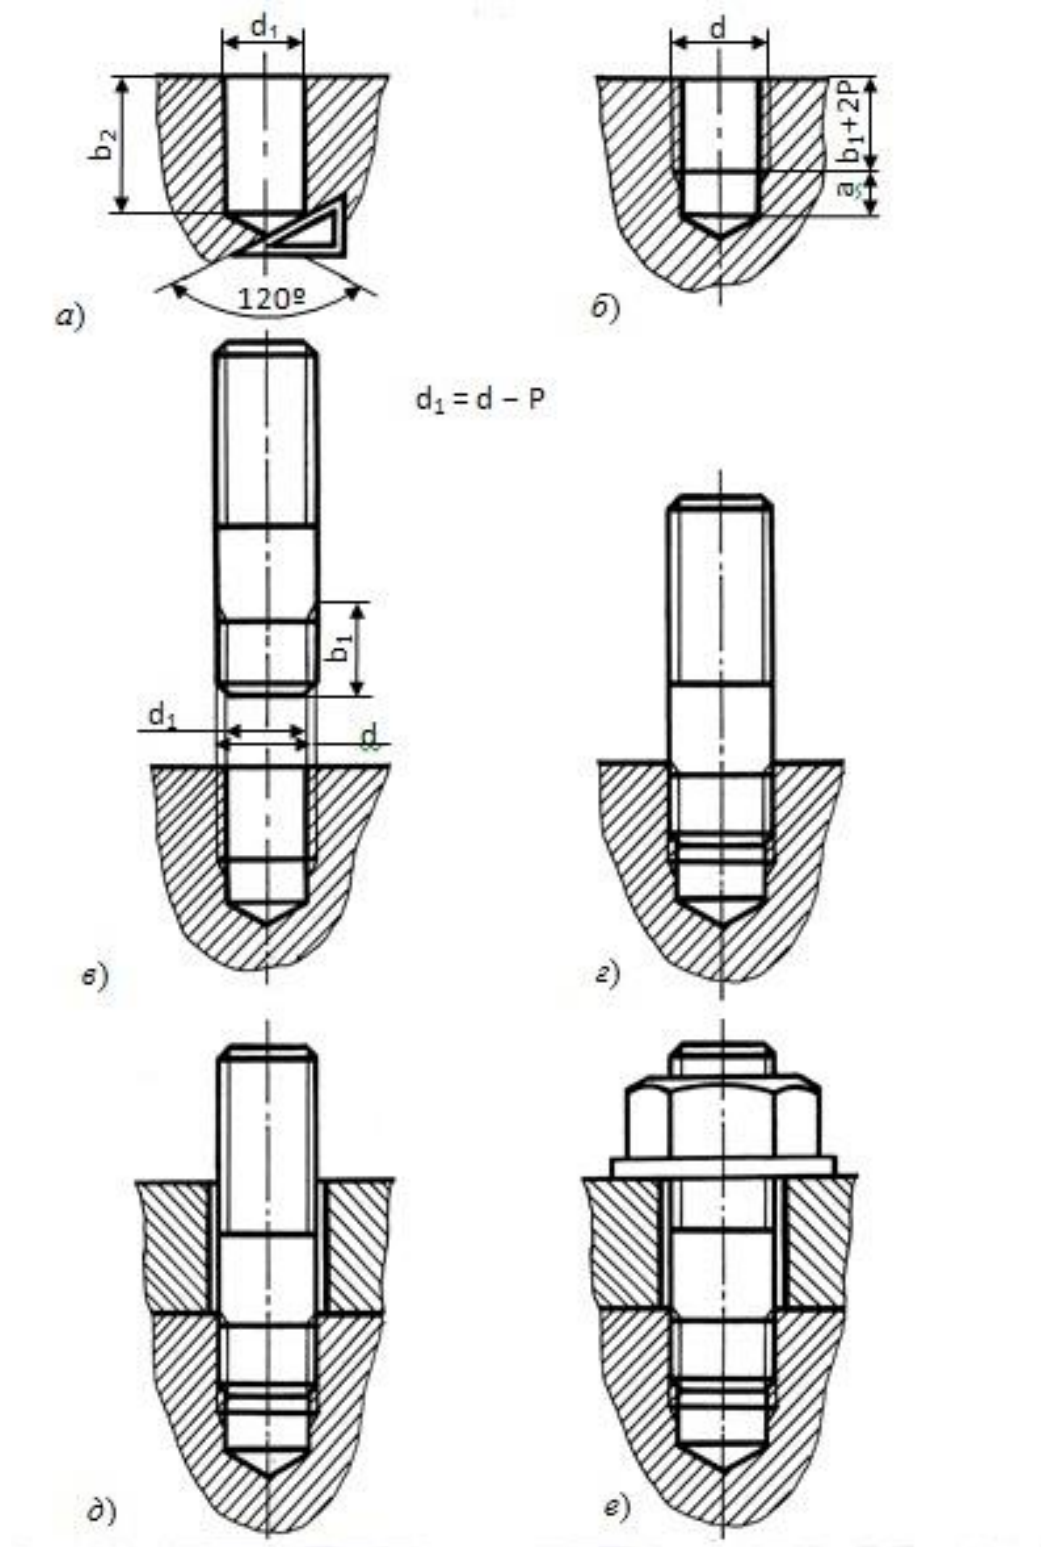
Технологическая последовательность выполнения отверстия с резьбой под шпильку и порядок сборки шпильчного соединения
